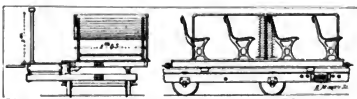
Vue latérale et vue longitudinale des deux plates-formes mobiles.
